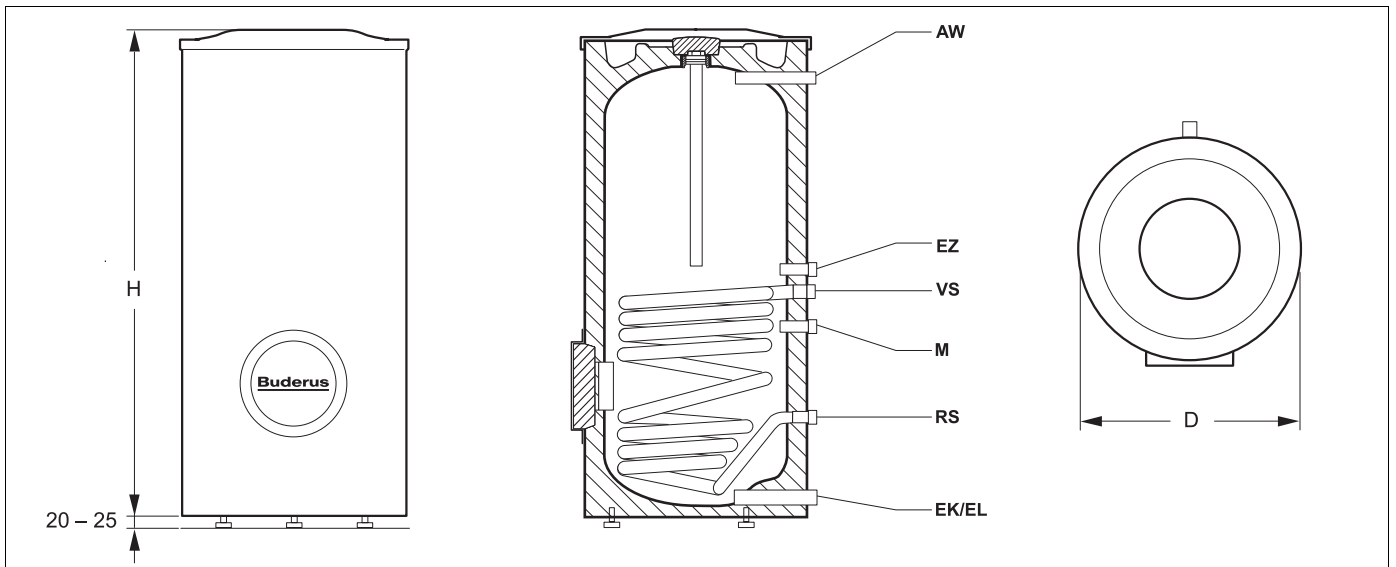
Abmessungen und Anschlüsse (Maße in mm) – Prinzipabbildung
